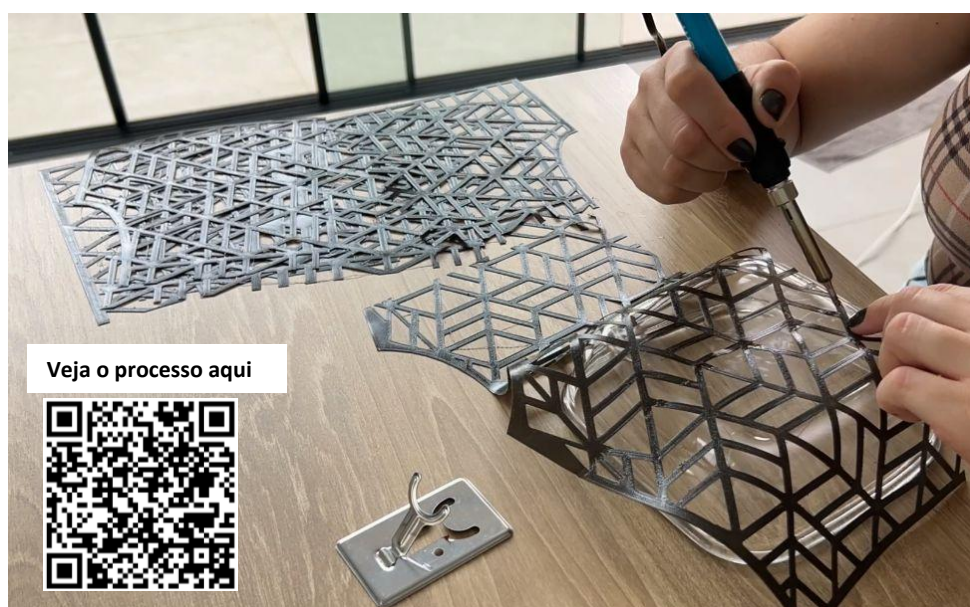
Ferro de solda utilizado na união das partes da peça.
